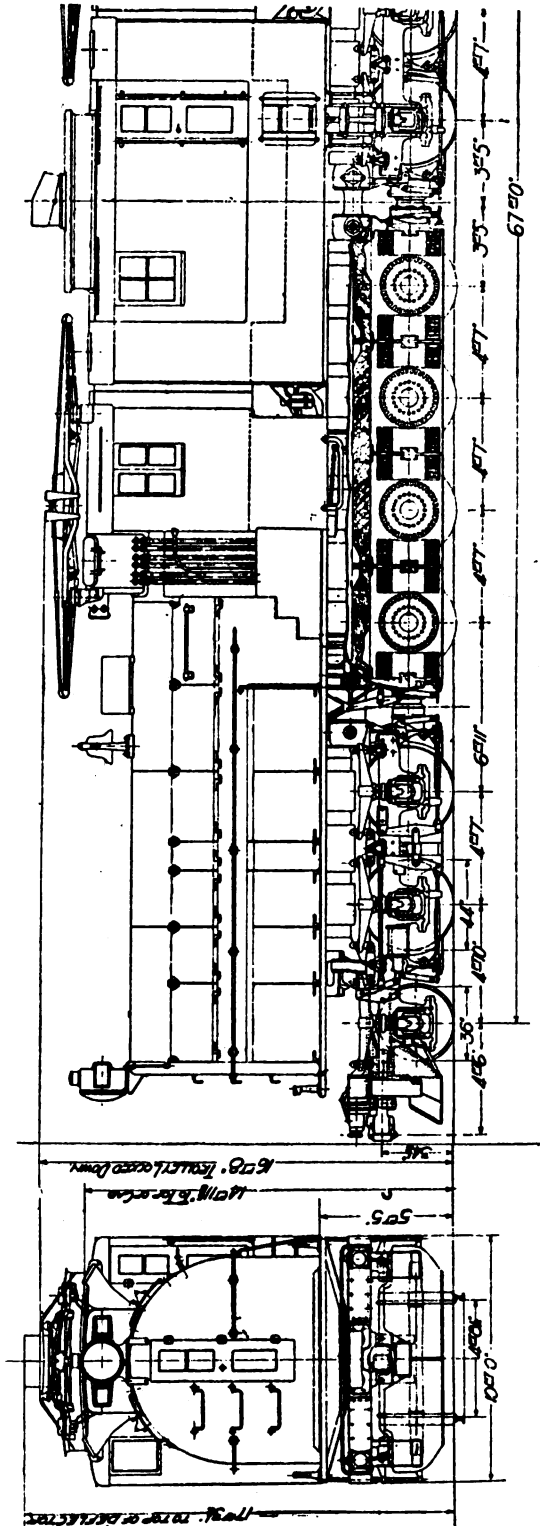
Vista laterale; vista e sezione longitudinali.
